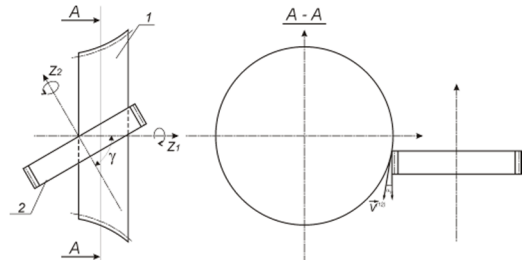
Схема формообразования квазиглобoidной заготовки
